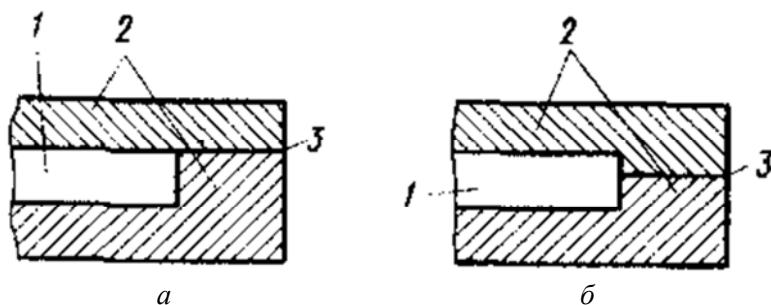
Расположение поверхности разреза кокиля по отношению к стенке отливки
